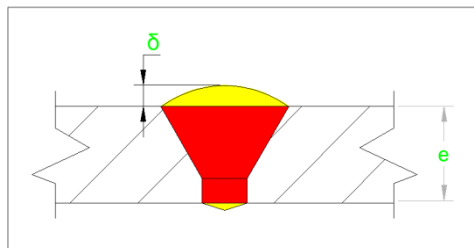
Reforzamiento de soldadura longitudinal
